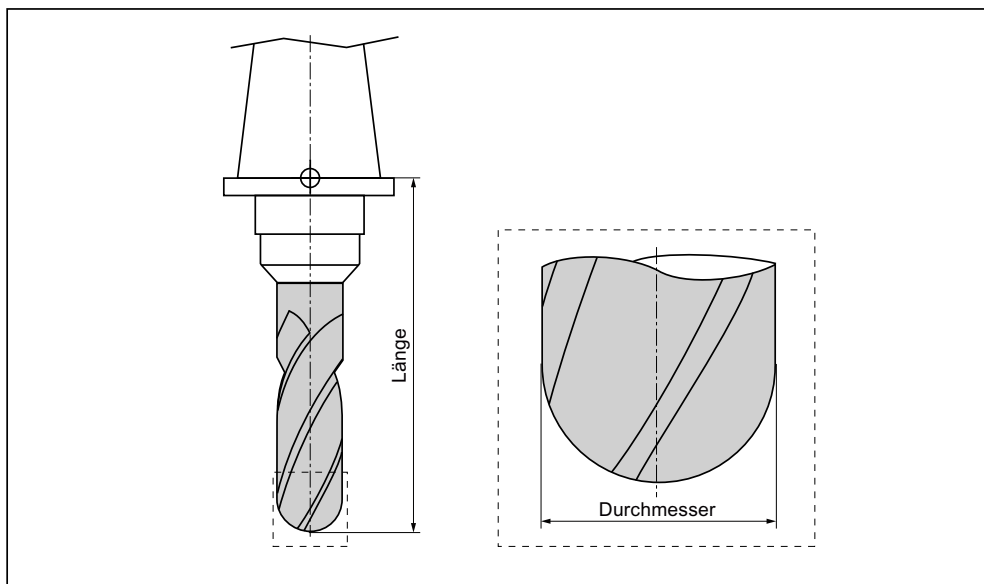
3D-Werkzeug am Beispiel eines zylindrischen Gesenkfräsers (Typ 110)
